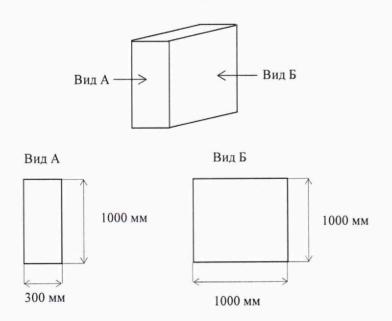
Внешний вид имитатора габаритных размеров № 4
